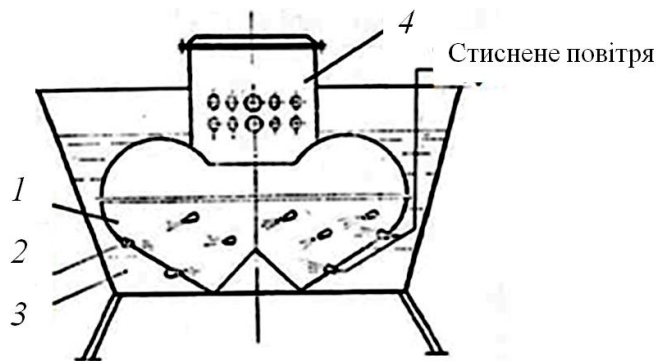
Схема реалізації способу гідроабразивної струйно-відцентрової обробки: 1 – робоча камера; 2 – струменеві апарати; 3 – ємність; 4 – горловина
